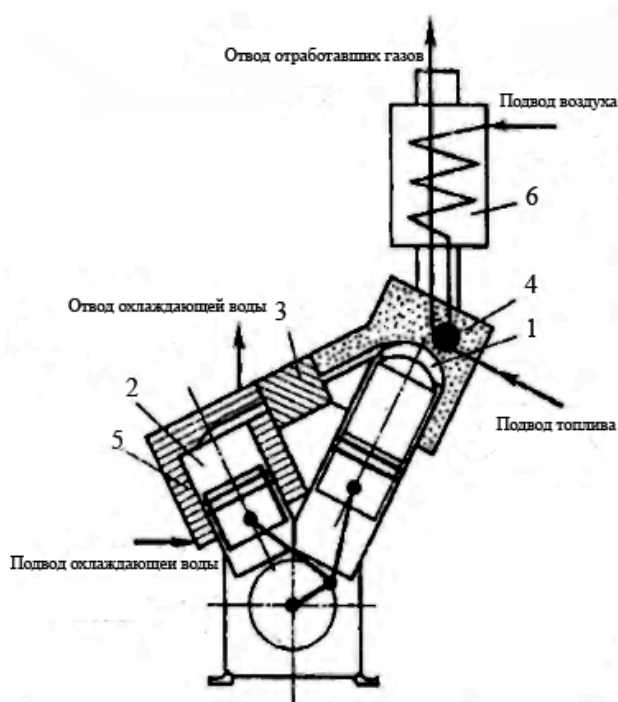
Схема двигателя Стирлинга с V-образным расположением поршней:
